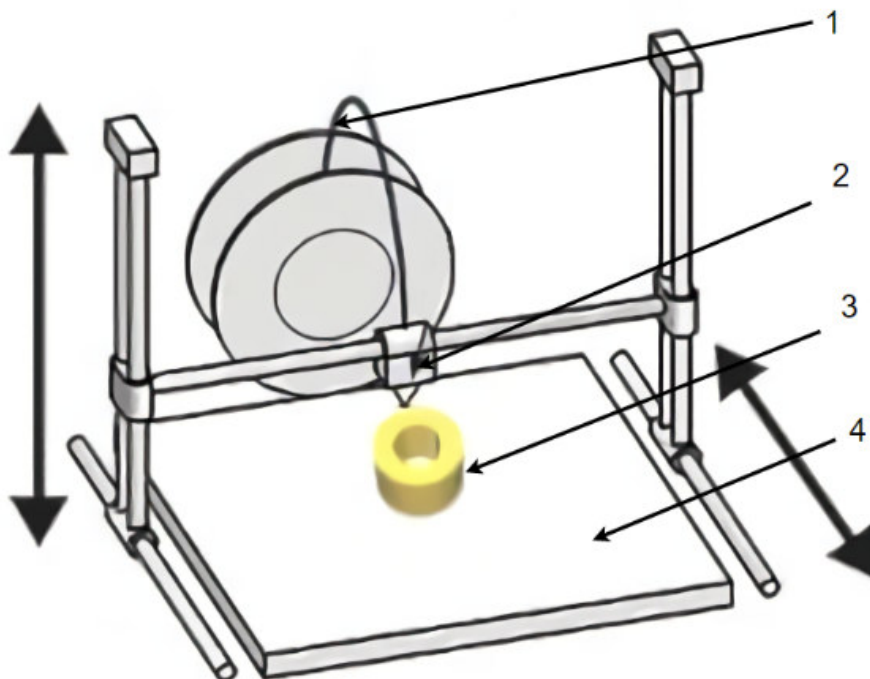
Схема 3D-принтера Anycubic Mega S: 1 – металлополимерная нить; 2 – сопло и нагревательный элемент; 3 – печатаемая втулка; 4 – платформа для печати
